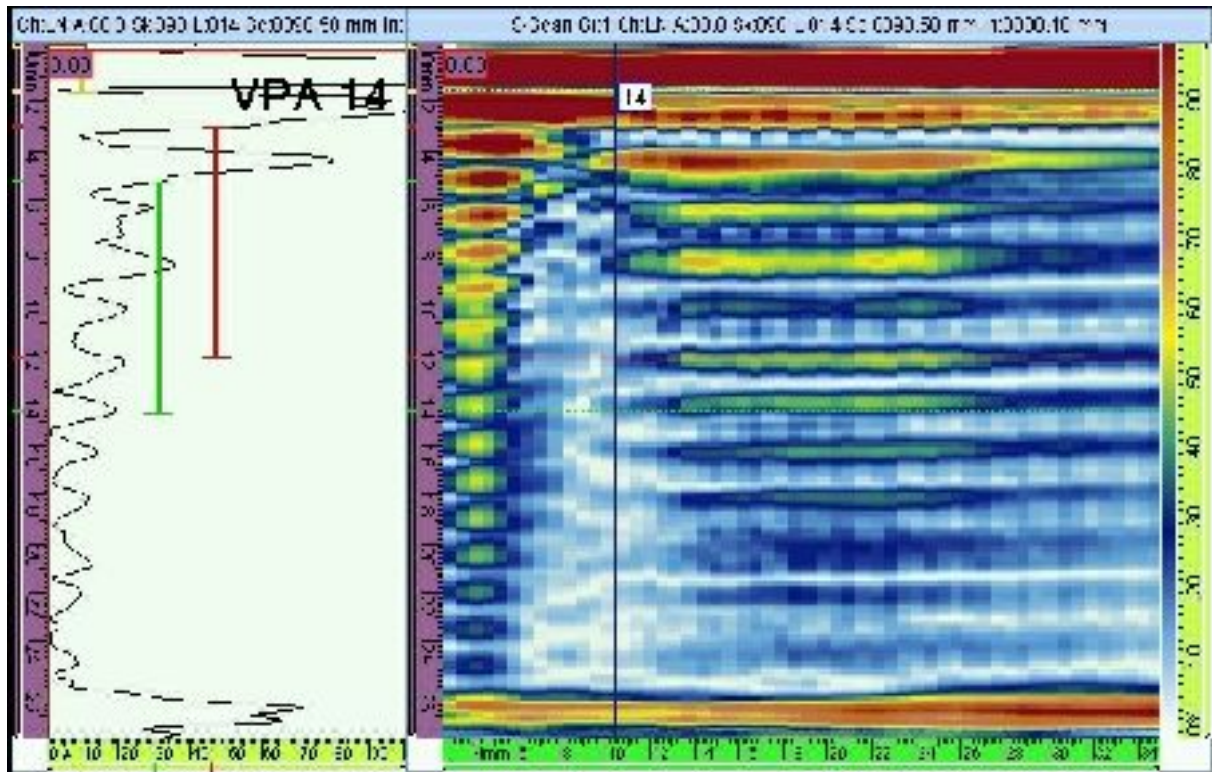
Válec A, pozice 1 spodní část válce. Je vidět ob násobné echa od vložky. Špatné spojení.
